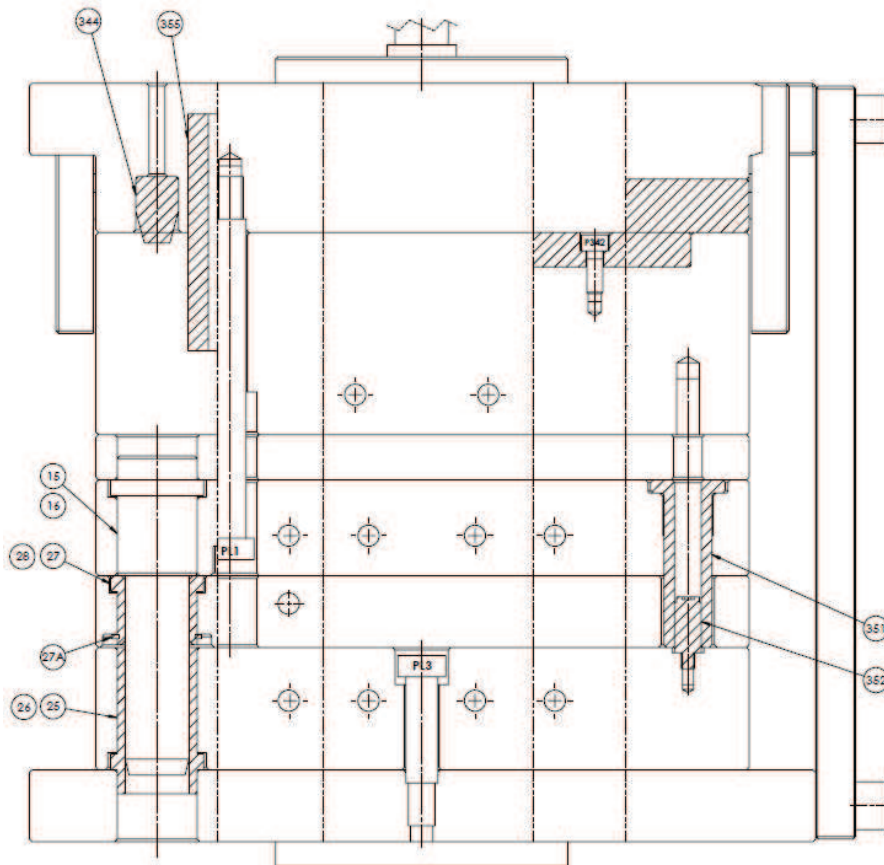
Molde de injeção com indicação dos vários componentes do molde 828 (vista em corte: seção C-C (desenho 2D final para montagem)).
